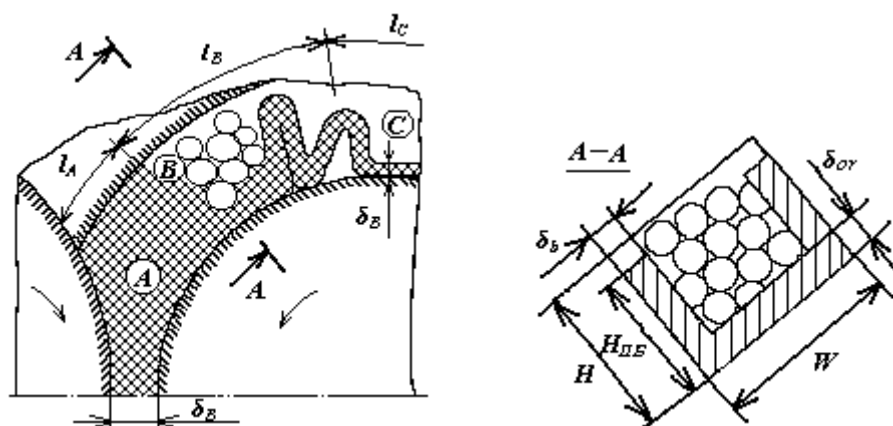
Схема процесса плавления в рабочих зонах двухчервячного экструдера
